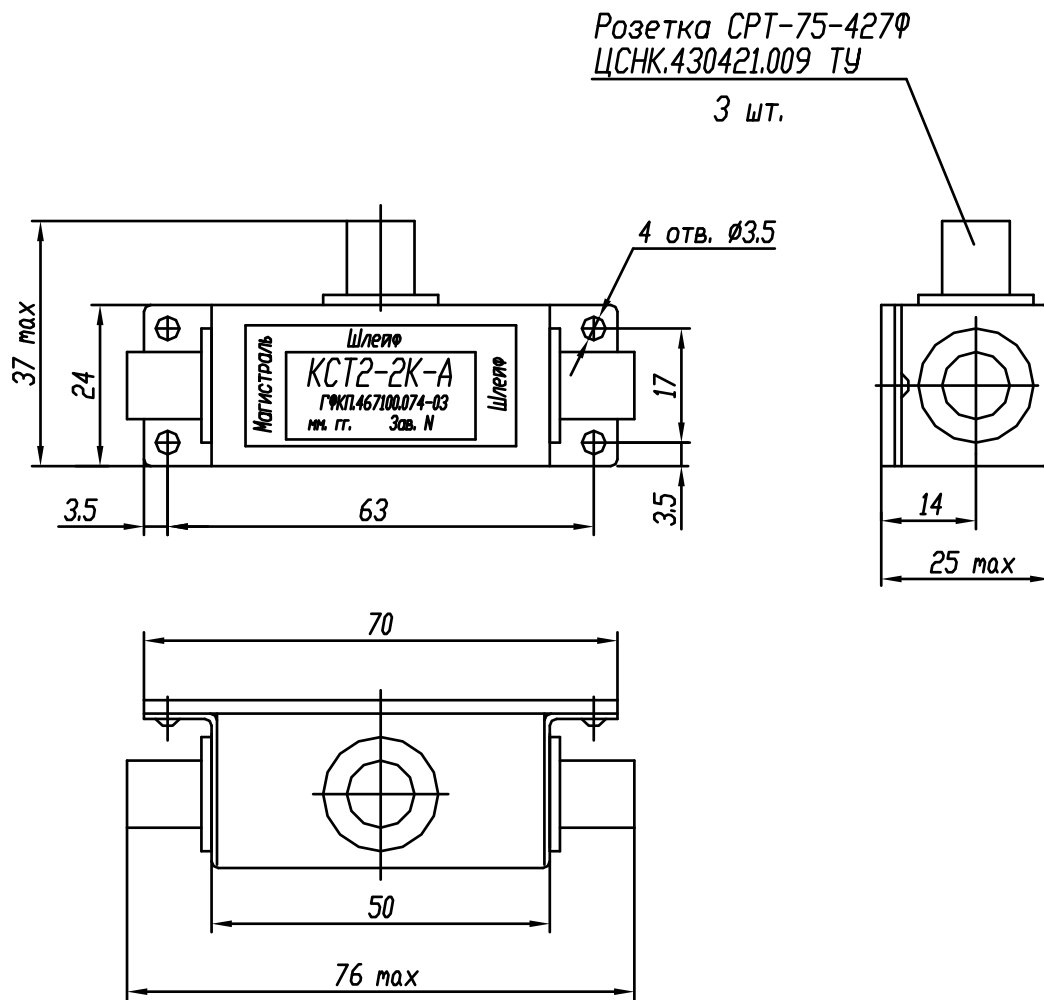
Габаритный чертеж коробки соединительной КСТ2-2К
